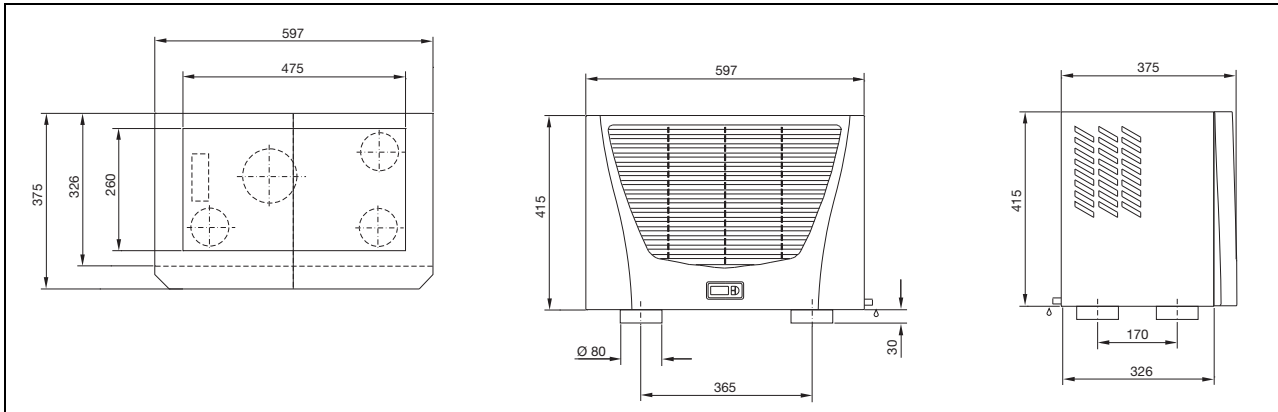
3359.xxx, 3382.xxx para montagem no teto
